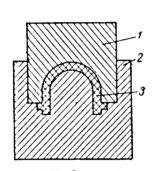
Схема обратного прессования: J — матрица; 2 - пуансон; 3- изделие.
